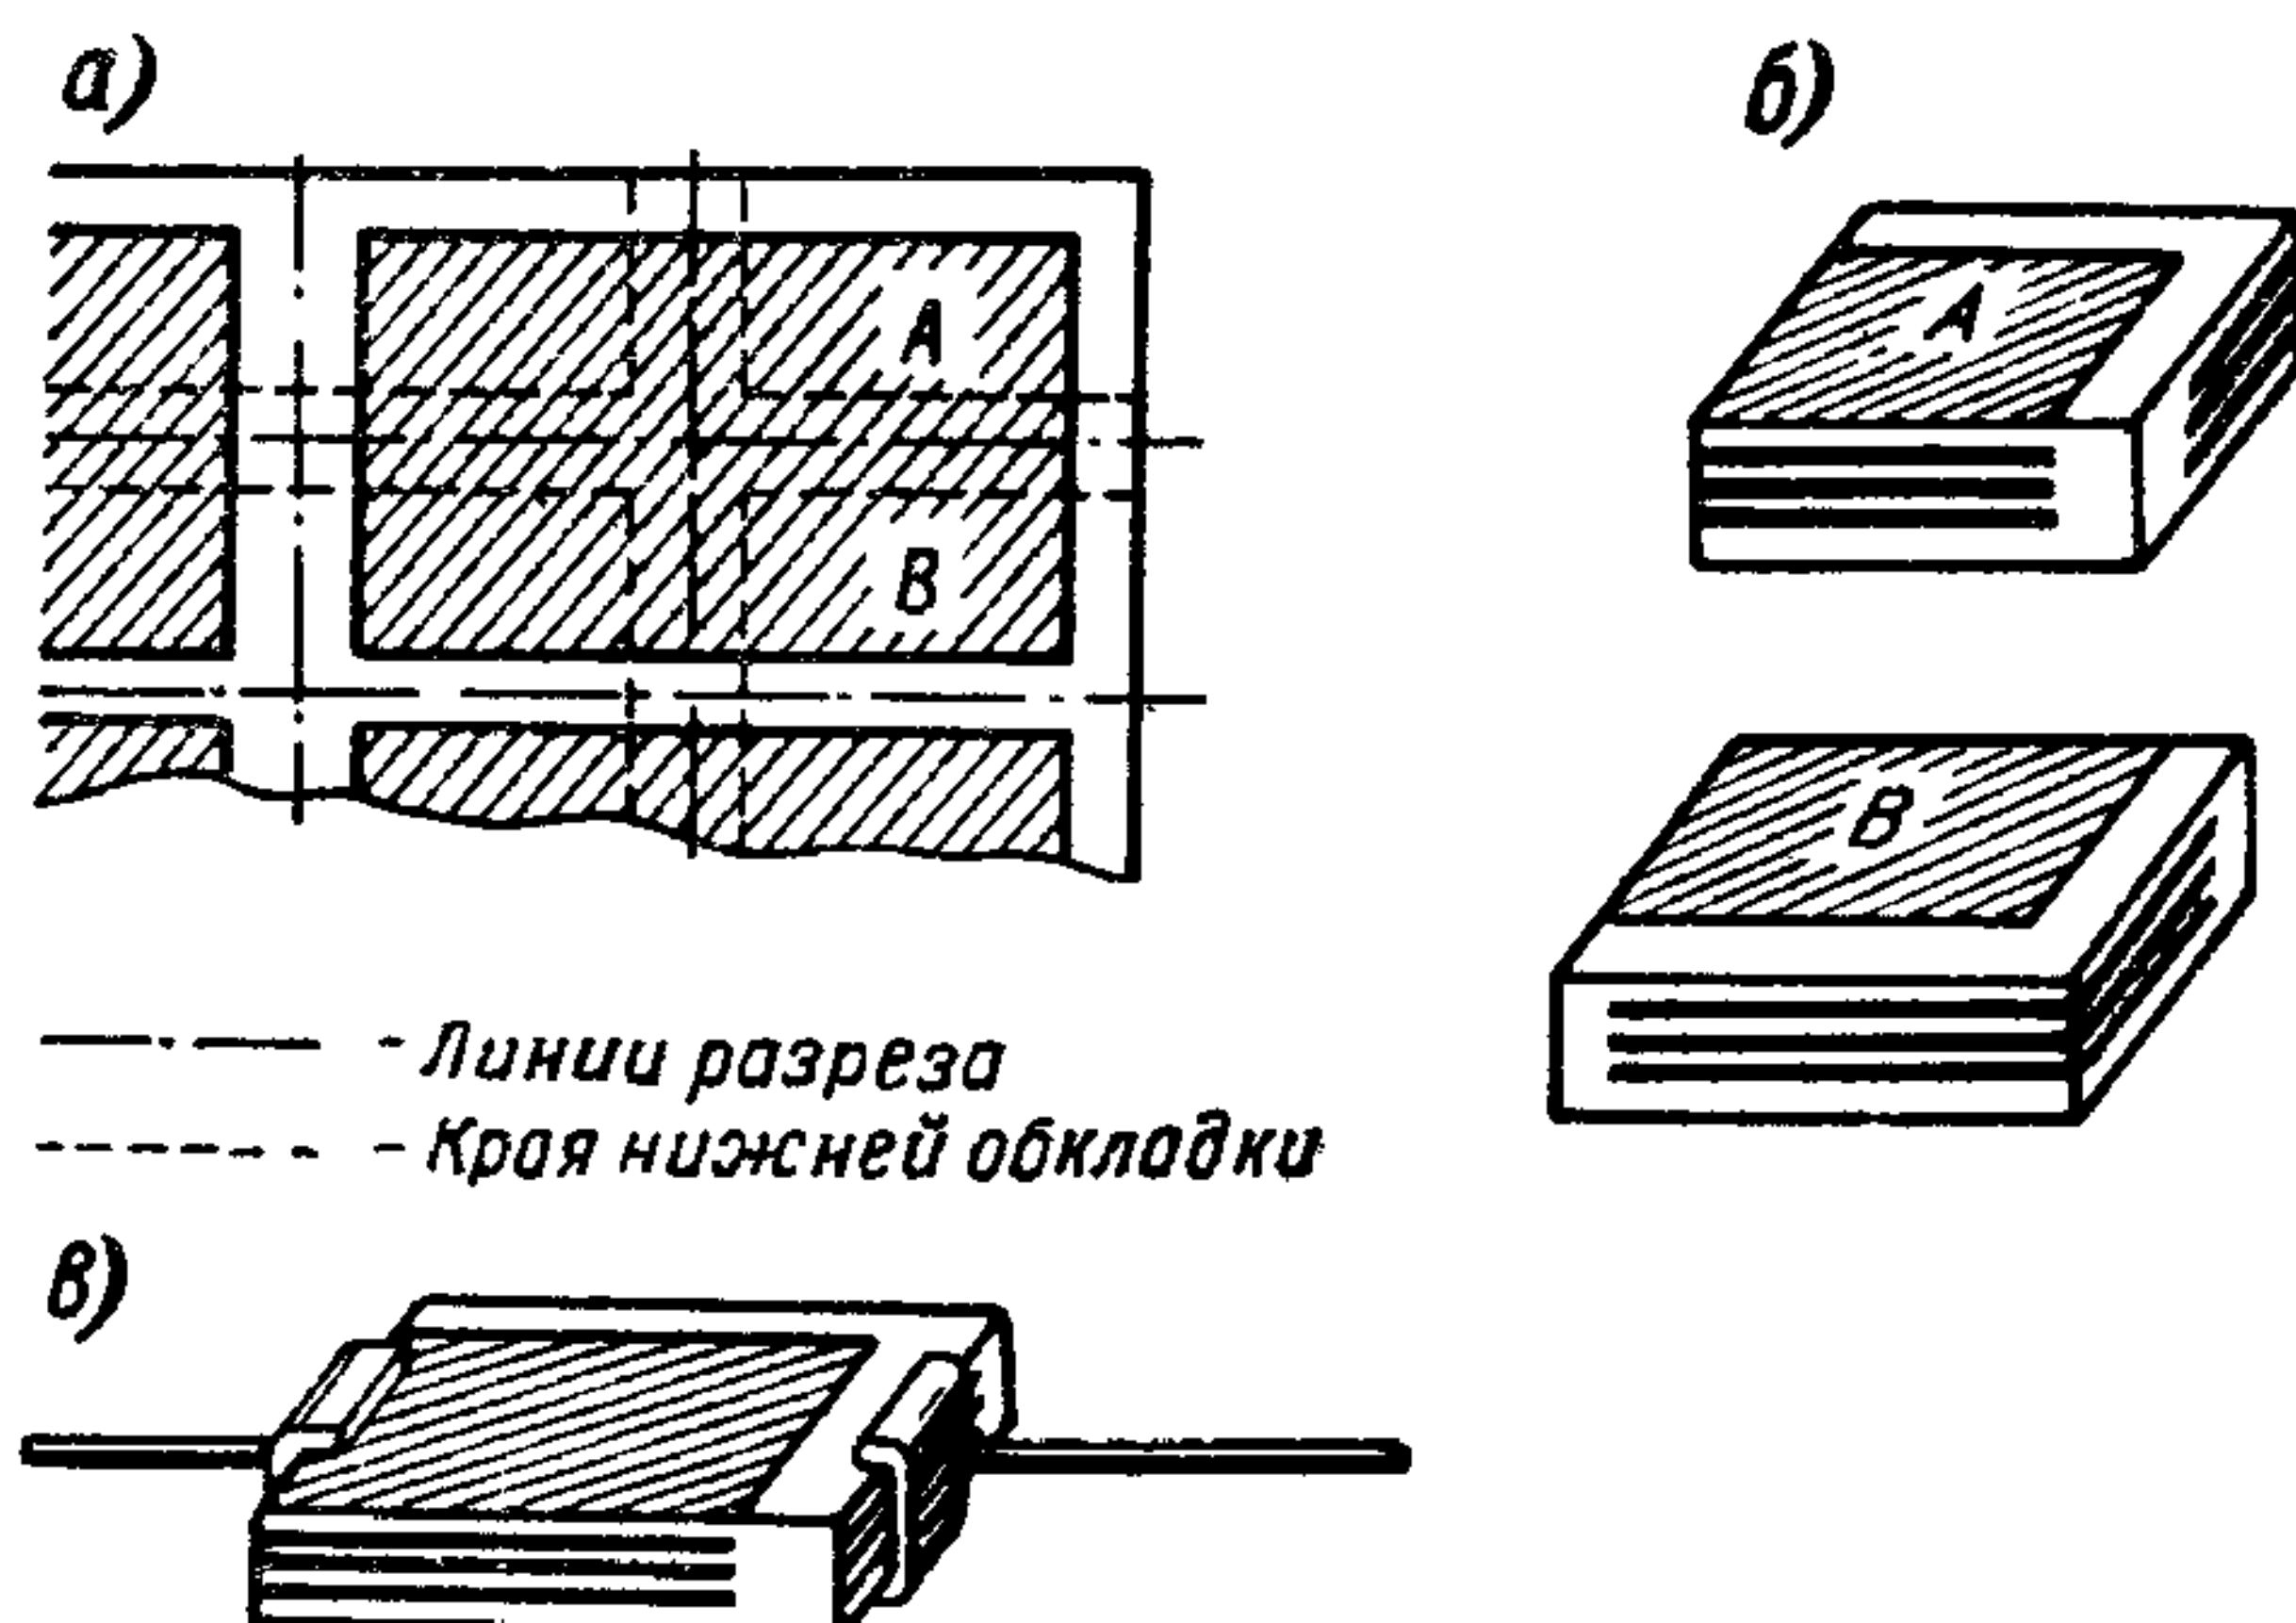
Стеклоэмалевые конденсаторы: *а* — заготовка до разрезки; *б* — куски разрезанной заготовки; *в* — конденсатор с припаянными выводами.
